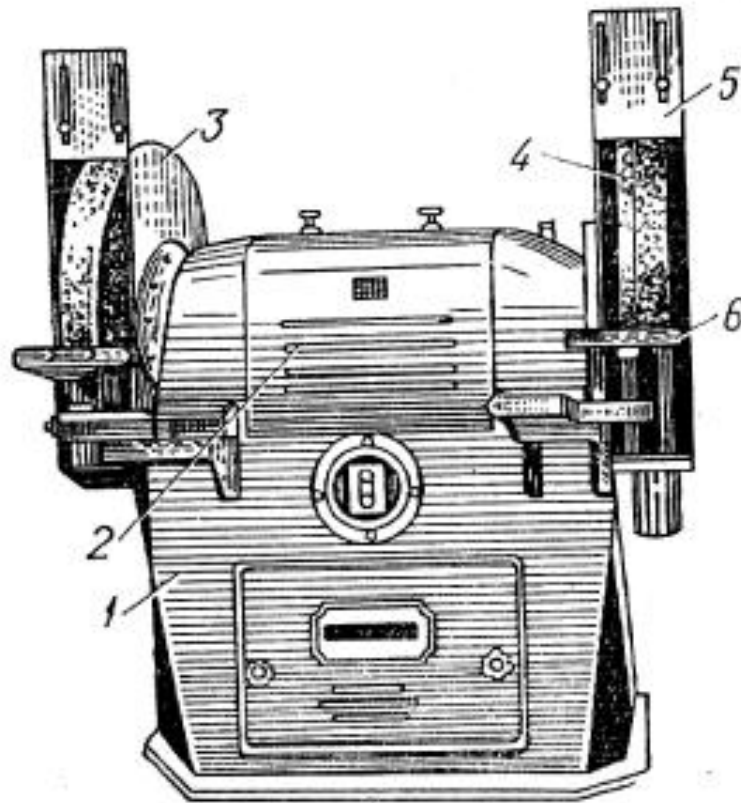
Заточувальний верстат: 1 – основа; 2 – електродвигун; 3 – кожух; 4 – шліфувальний диск; 5 – щитки; 6 - підручники
